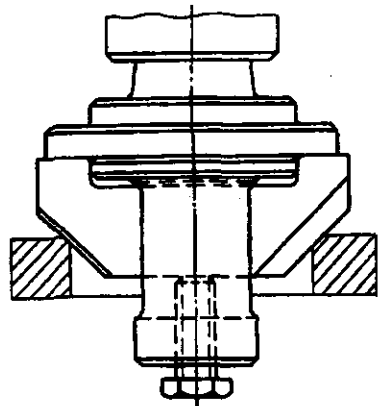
Пластинчатая зенковка для снятия фаски в отверстия большого диаметра
